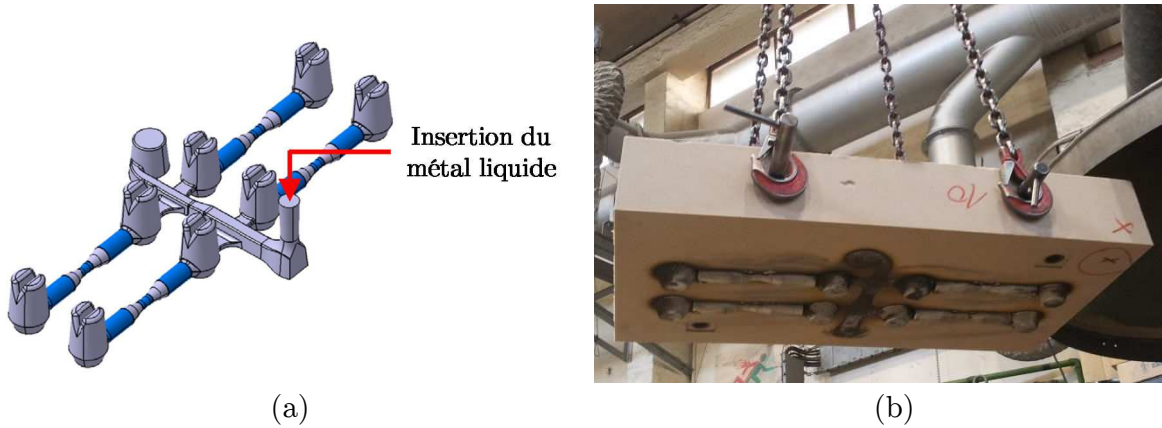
(a) Configuration de la grappe de coulée des éprouvettes, (b) éprouvettes refroidies dans le moule
